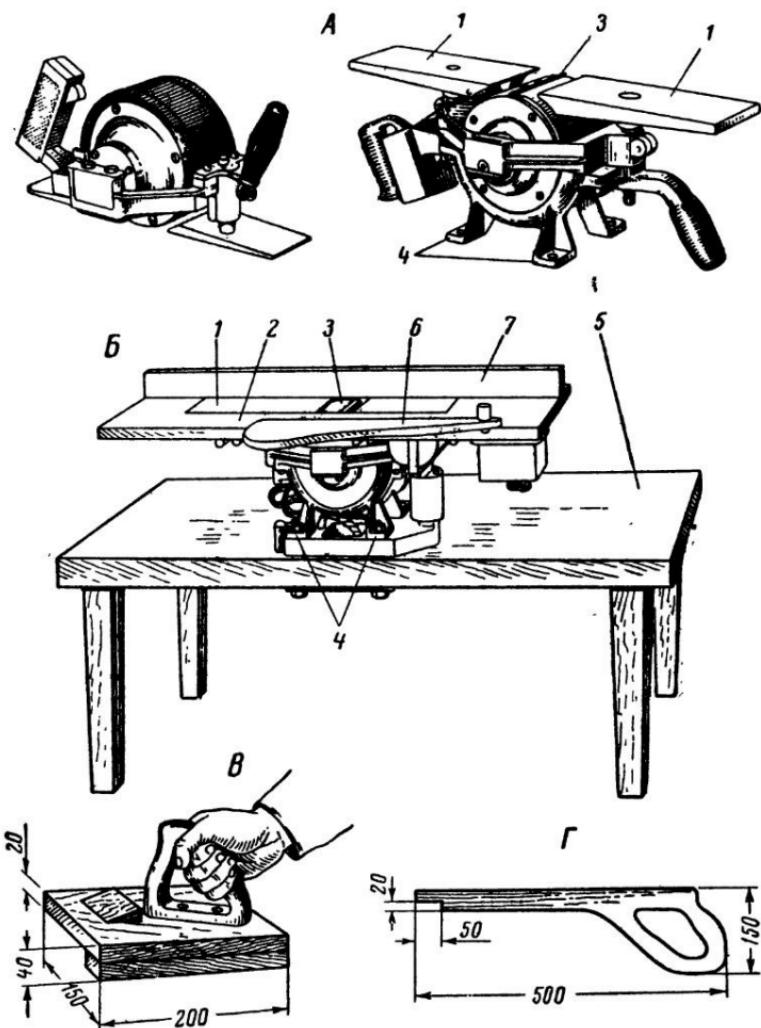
Электрорубанки: А — рубанки как механизированные инструменты; Б — рубанок — строгальный станок (1 — опорные плоскости инструмента, 2 — рабочая поверхность стола, 3 — ножевой вал, ограждение сдвинуто, 4 — опорные лапки, 5 — стол-верстак, 6 — ограждение, 7 — упор для обрабатываемой заготовки); В — толкател для фуговки мелких деталей; Г — толкатель.
